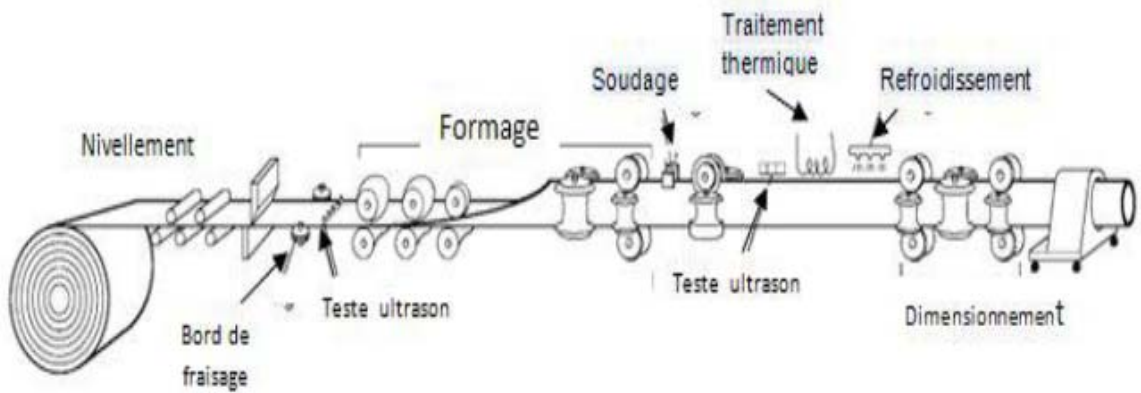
Technique de fabrication des tubes soudés en spirale.
